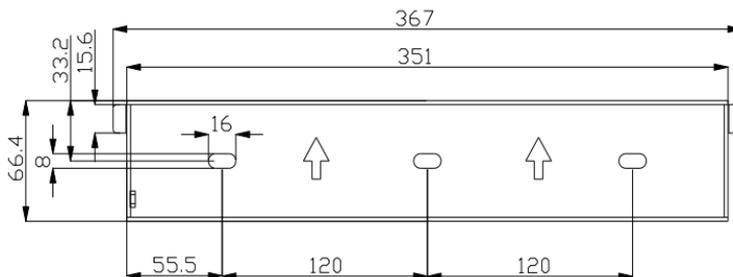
Dimensioni piastra di fissaggio del R5-4K/5K/6K/8K/9K/10K/12K-T2
